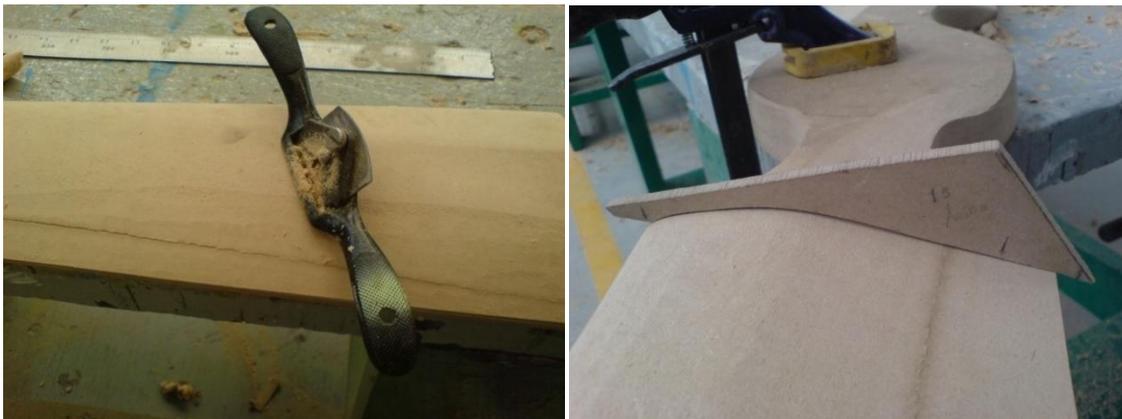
Desbastando con el cepillo tipo mariposa (escochebere) y colocando plantilla.
